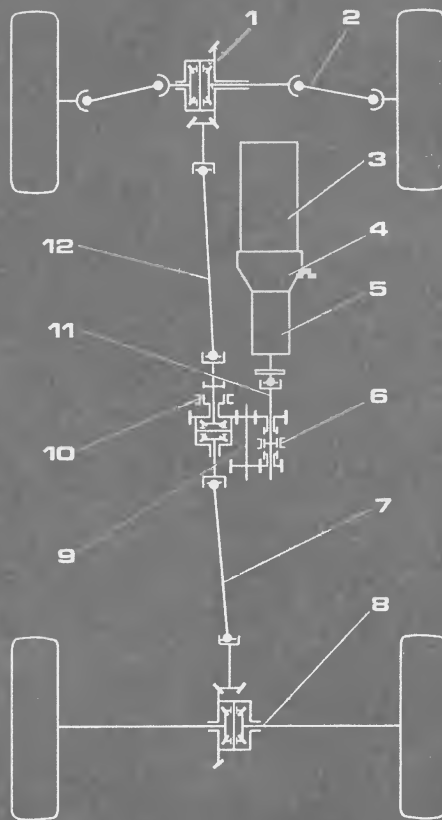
Схема трансмиссии ВАЗ—2121: 1 — передний мост; 2 — качающийся вал с шарнирами постоянной угловой скорости; 3 — двигатель; 4 — сцепление; 5 — коробка передач; 6 — муфта включения передач; 7 — задний карданный вал; 8 — задний мост; 9 — раздаточная коробка; 10 — муфта блокировки межосевого дифференциала; 11 — промежуточный карданный вал; 12 — передний карданный вал.
